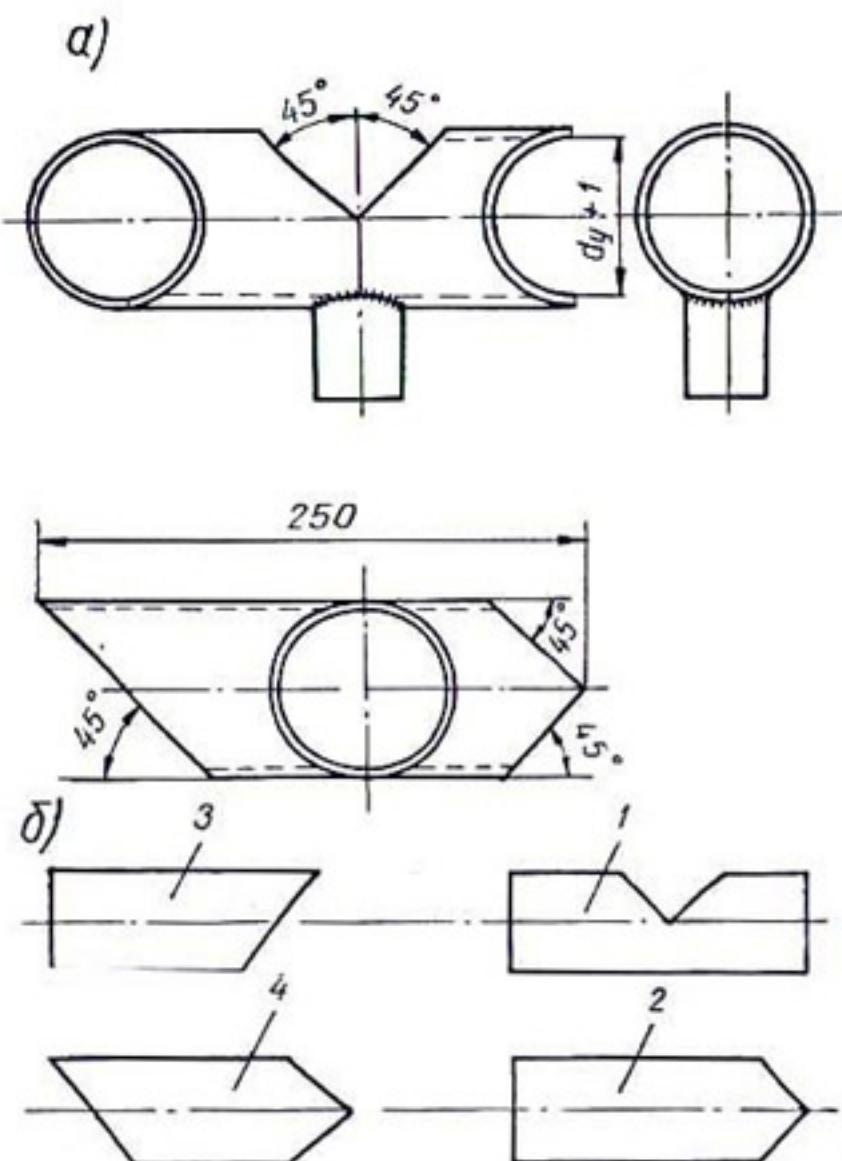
Схема шаблона и заготовляемых на нем деталей:
